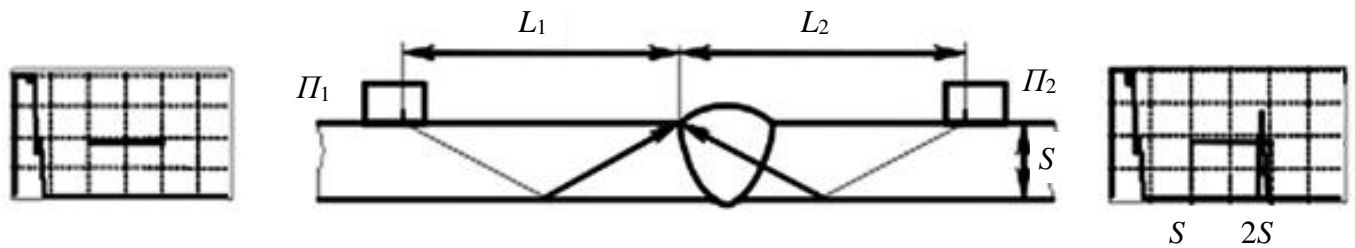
Схема расшифровки ложных эхо-сигналов от валика усиления сварного шва
